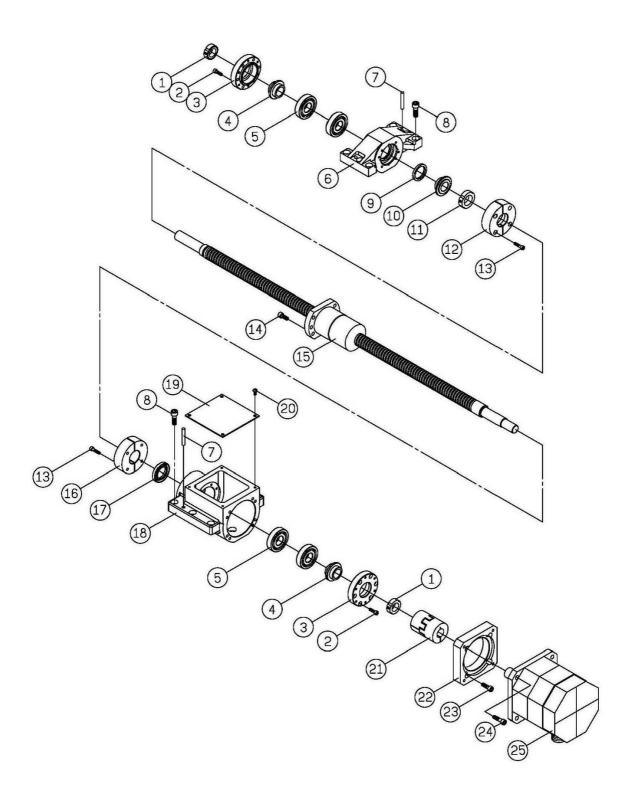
Baugruppe X-Achse - Assembly X-Axis
